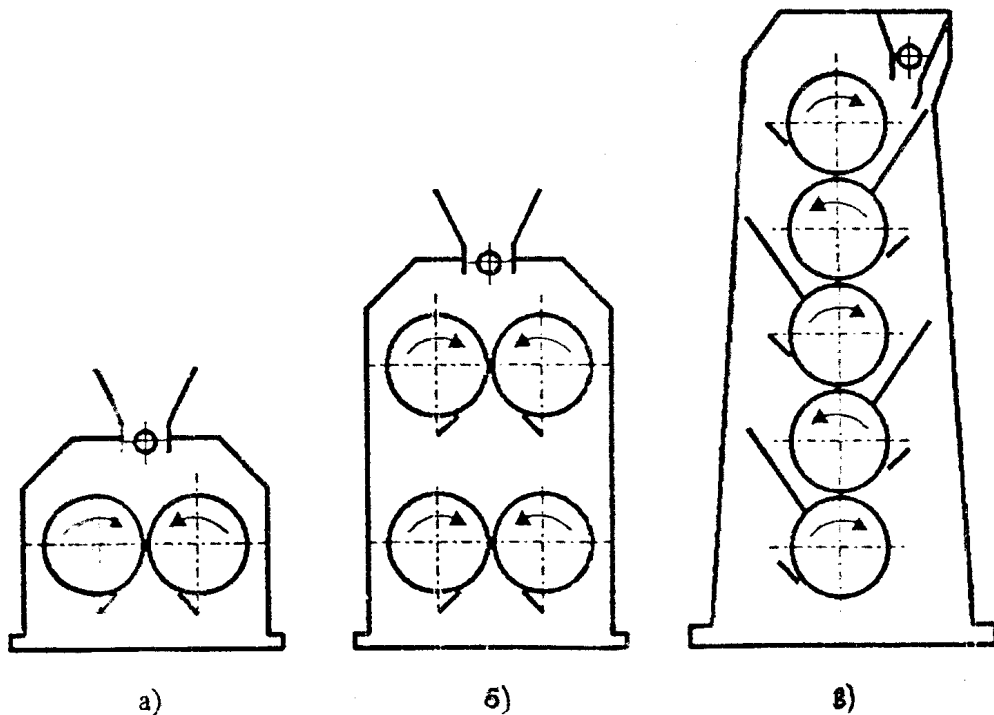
Схеми конструкцій вальцевих верстатів: а) – однопарний; б) – двопарний; в) – п'ятивальцевий: 1 – станина; 2 – валець; 3 – бункер завантажувальний; 4 – живильний валик.
